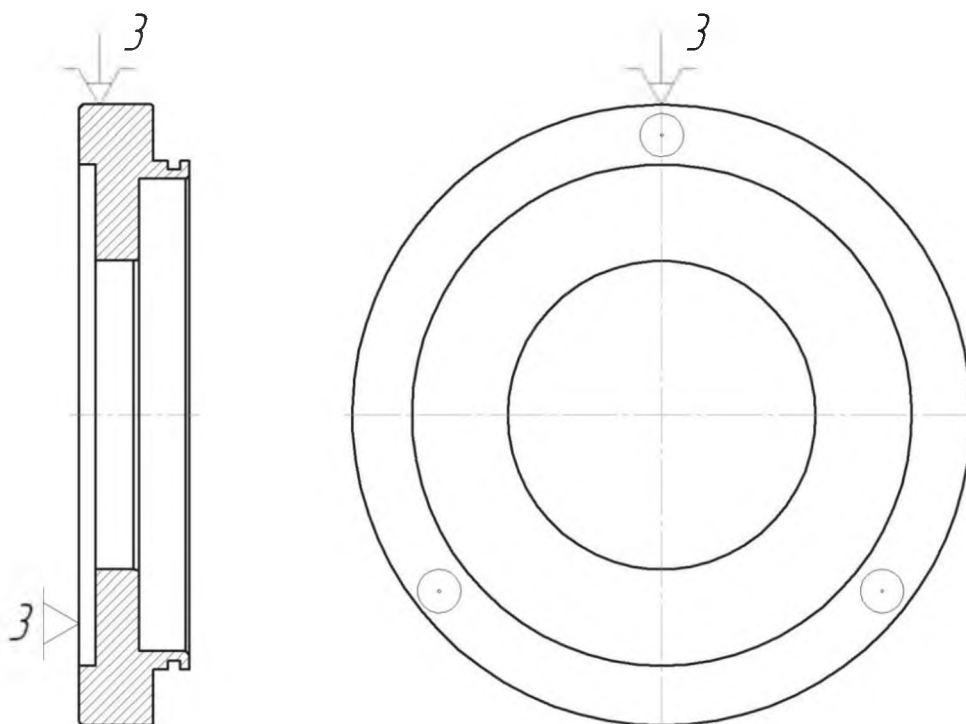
Схема базування на токарному верстаті (Установ А)
